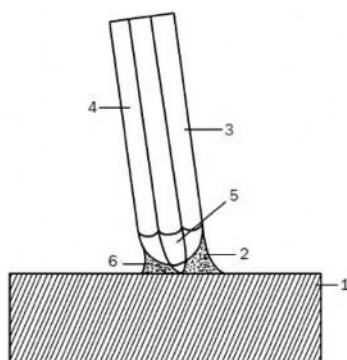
Схема горения сварочных дуг при сварке трехфазной дугой: 1 – основной металл; 2, 6 – дуга между электродом и металлом; 3, 4 – электрод; 5 – дуга между электродами
